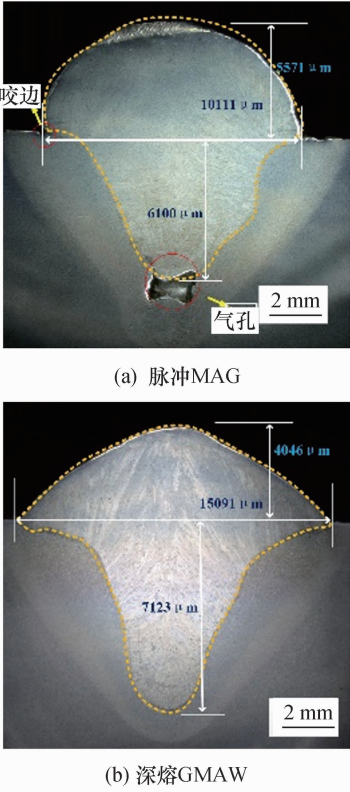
不同焊接模式的焊缝成型及参数测量
